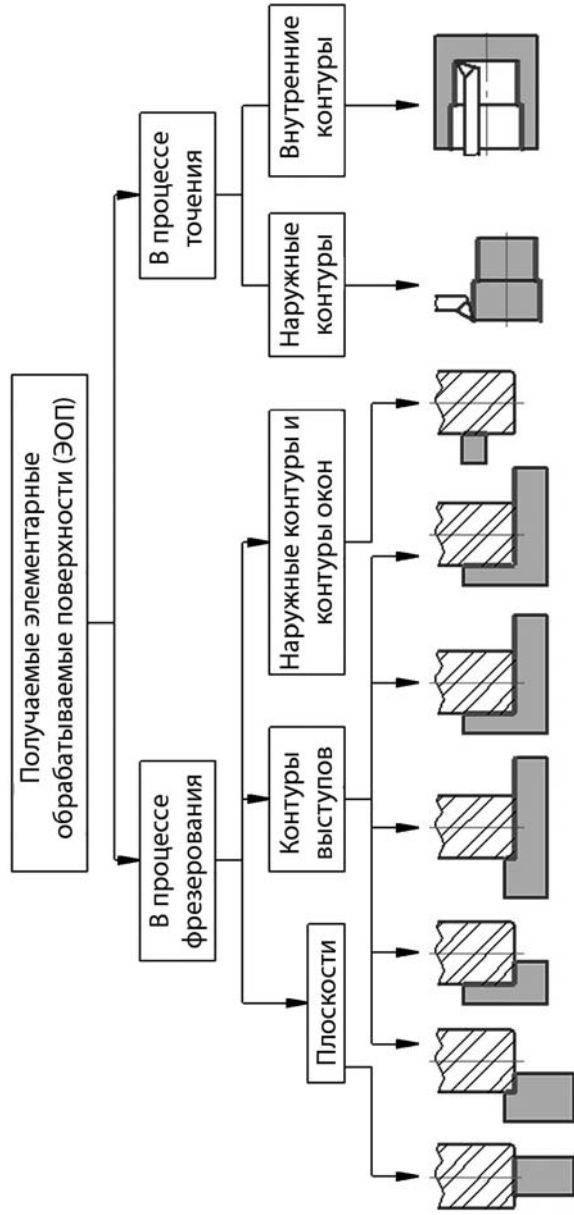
Виды элементарных обрабатываемых поверхностей (ЭОП) при фрезеровании и точении
